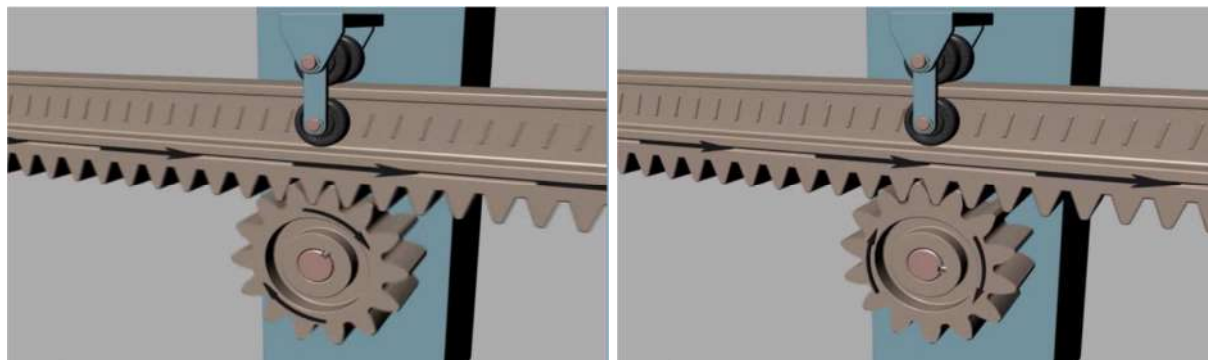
3D-модель рейкової передачі (рейка рухома)
